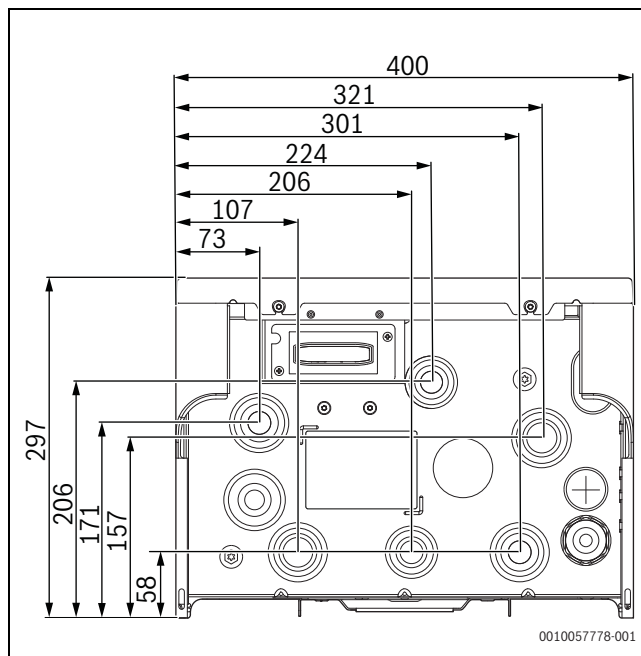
Dimensions, raccords, vue de dessous (mm)
